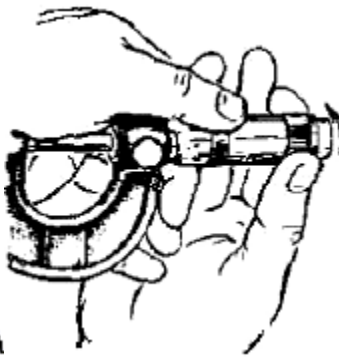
Закрепление барабана микрометра корпусом трещотки
